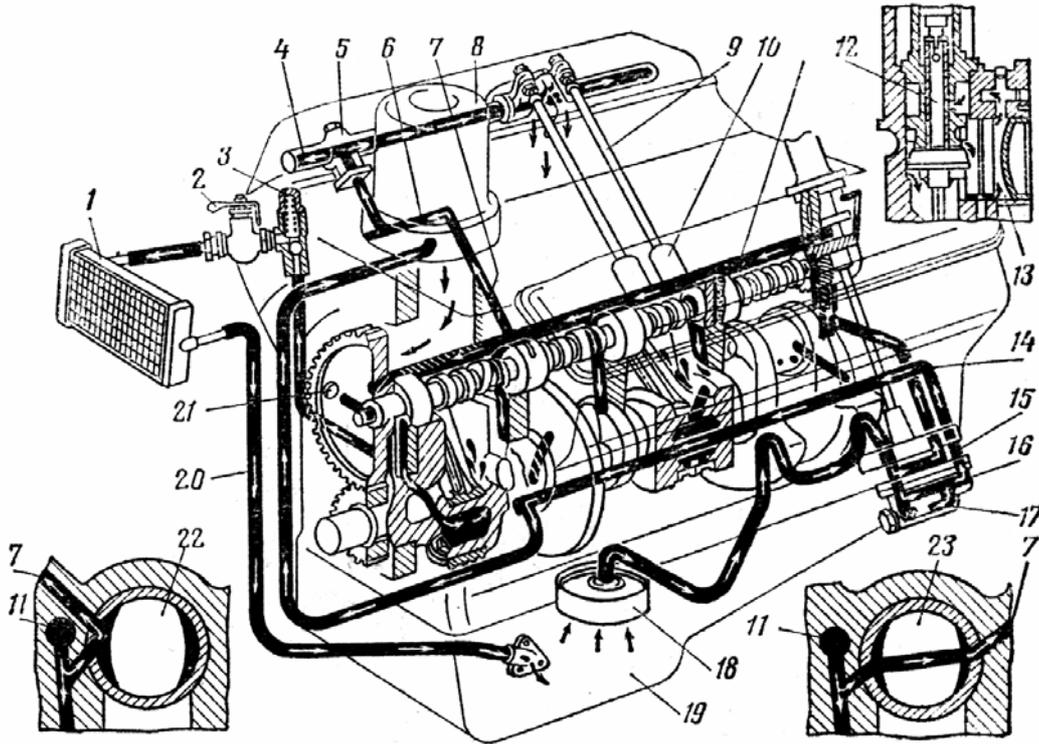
Схема смазочной системы двигателя ЗМЗ-53:
